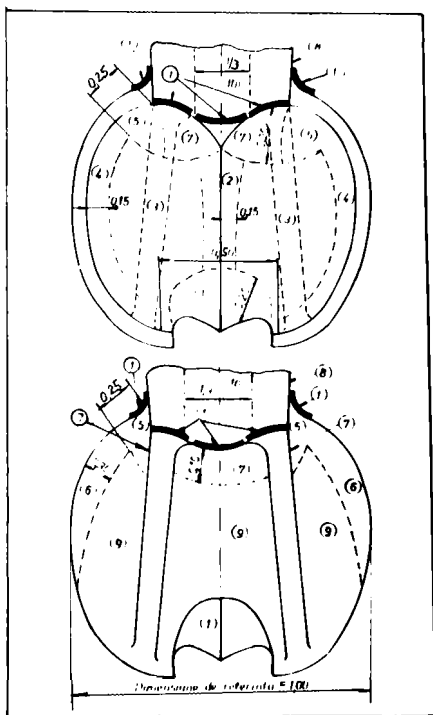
Zone de inspecție pentru rotoare Pelton.
